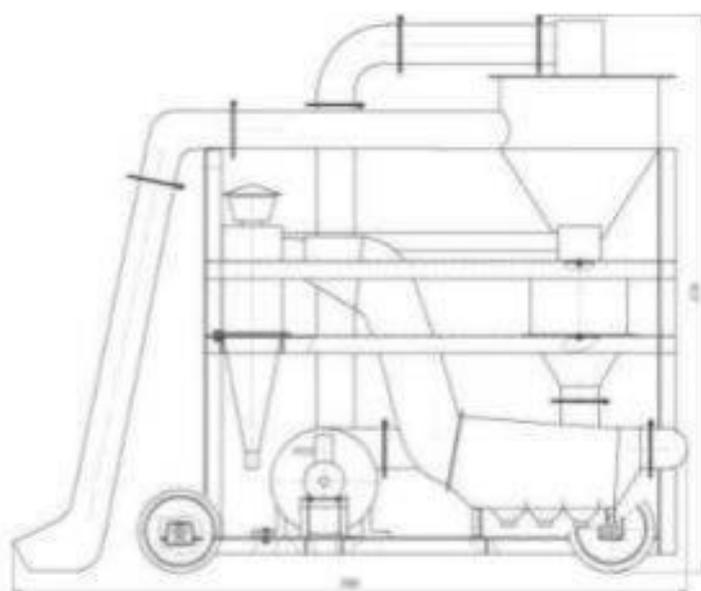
Схема предлагаемого устройства для обрушивания
